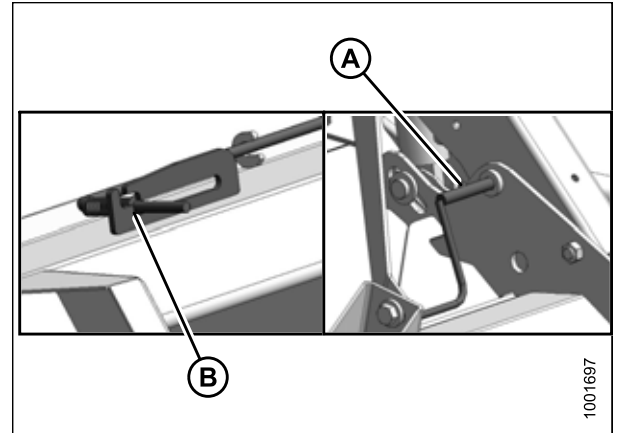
Предохранительный упор мотовила — центральный рычаг
